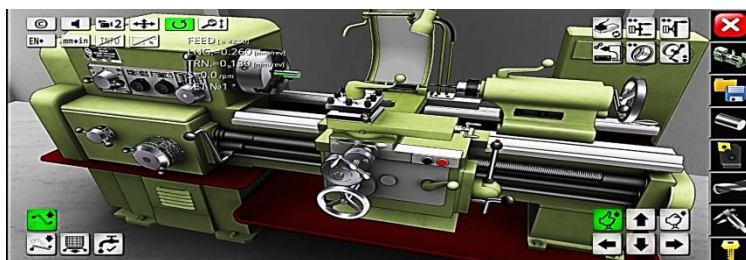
Симулятор токарного станка 1К62 Lathe Simulator Lite
